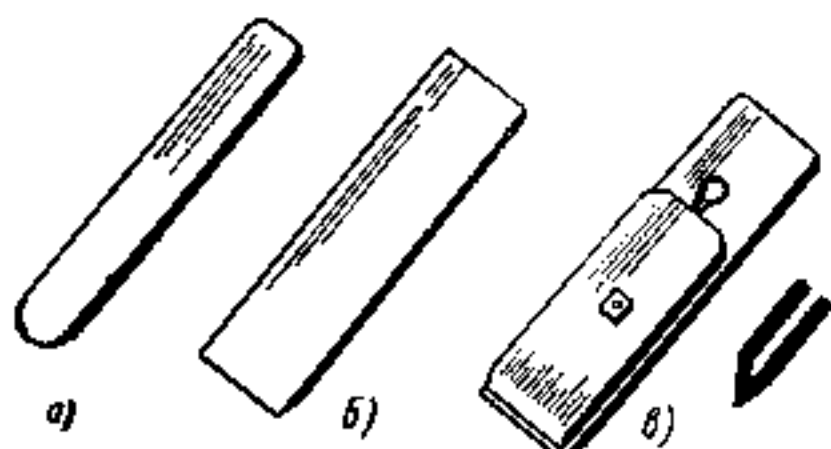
Железки: а) — шерхебеля, б) — рубанка, в) — двойного рубанка
